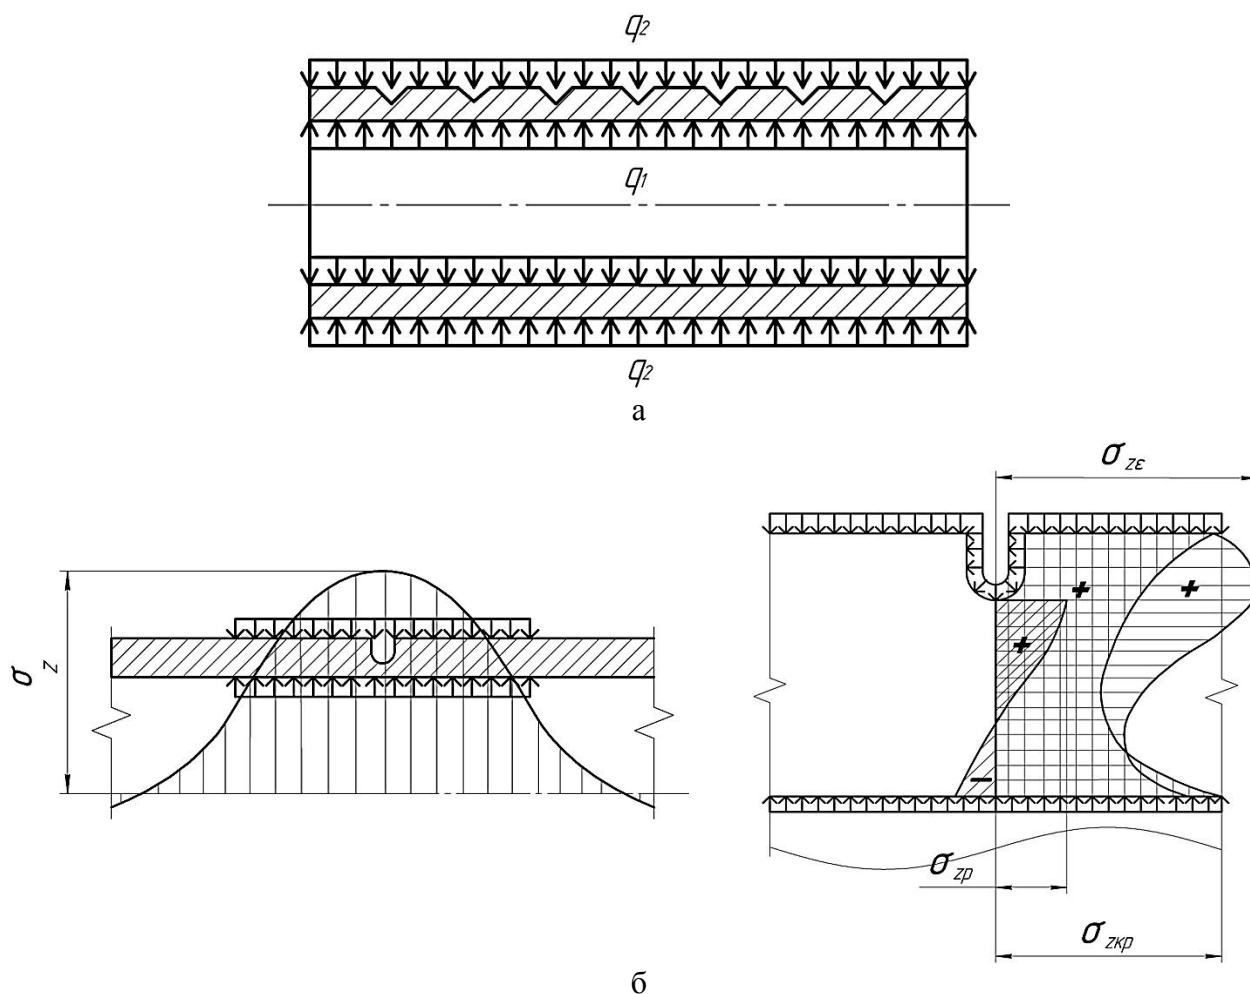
Схема нагружения (а) и эпюры распределения напряжений (б) в трубчатых заготовках при разделении ломкой [10]
